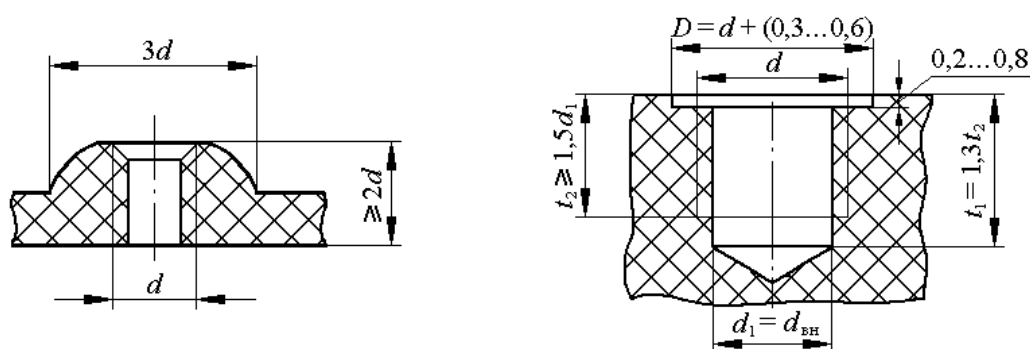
Элементы резьбовых соединений для сквозных и несквозных отверстий
